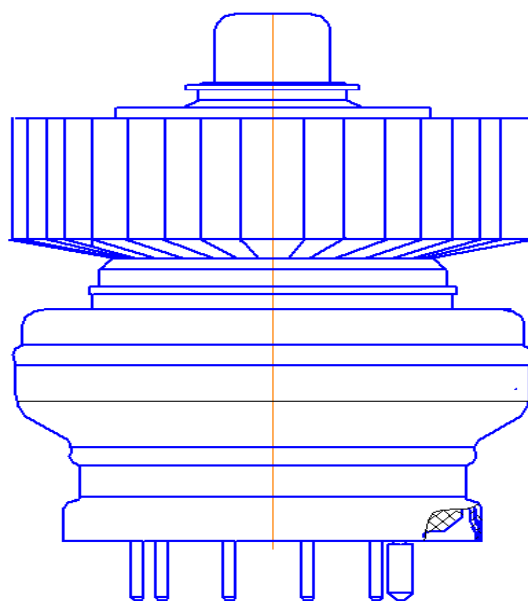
Чертеж общего вида лампы ГМИ-26Б
